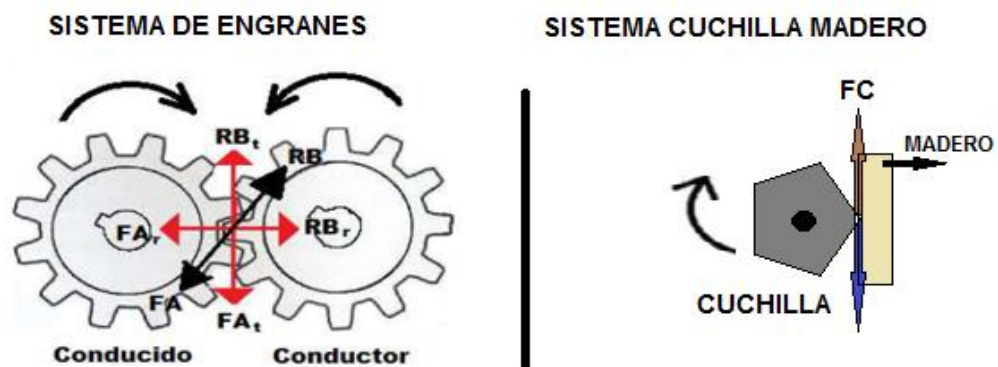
Fuerza de la cuchilla y ángulo de presión de los engranajes.
